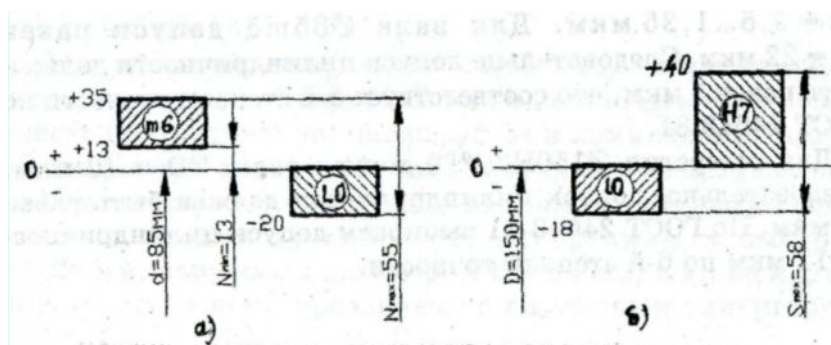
Схемы расположения полей допусков посадок подшипника: а) внутреннего кольца с валом; б) наружного кольца с корпусом
